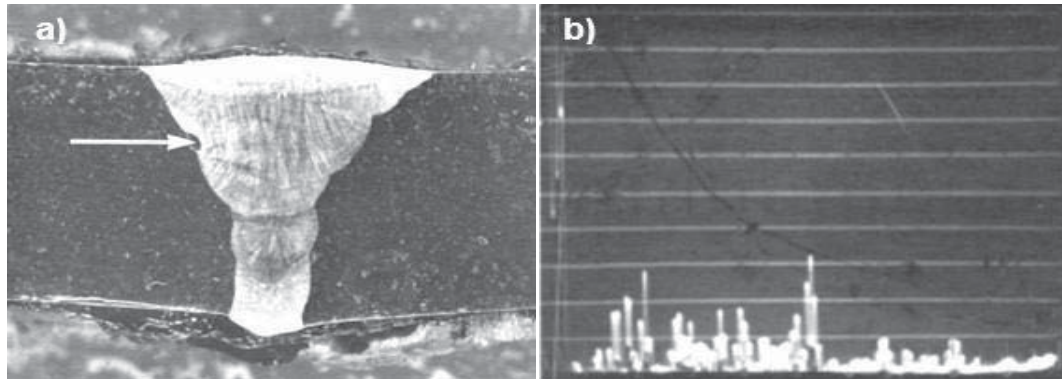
a) macrografía que muestra una inclusión de escoria dentro de la soldadura b) señal de ultrasonido característica de una inclusión de escoria en A-Scan.
